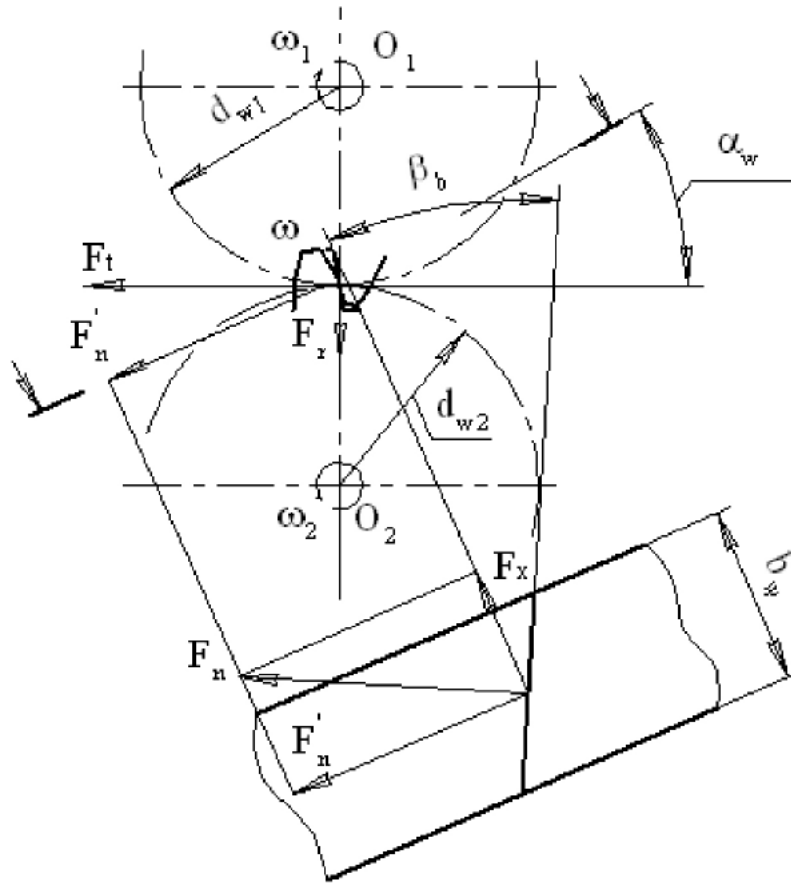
Схема сил в зацеплении цилиндрической зубчатой передач
